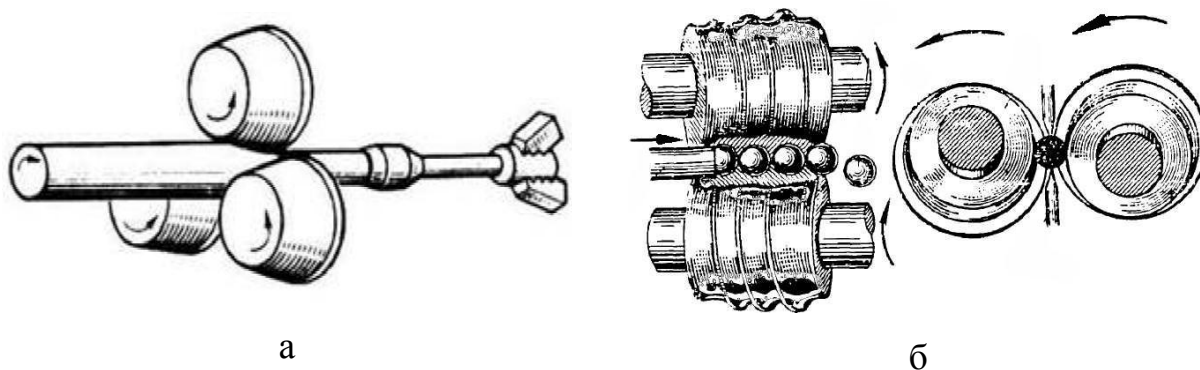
Схема поперечно-гвинтового прокатування:
